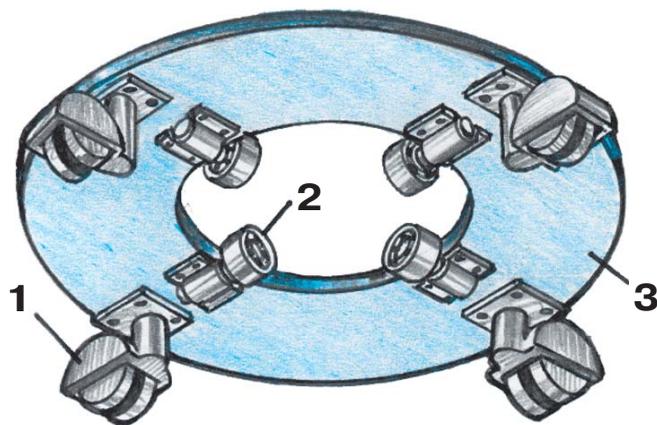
Платформа (вид снизу): 1 — ролик (4 шт.); 2 — шарикоподшипник (4 шт.); 3 — платформа.
